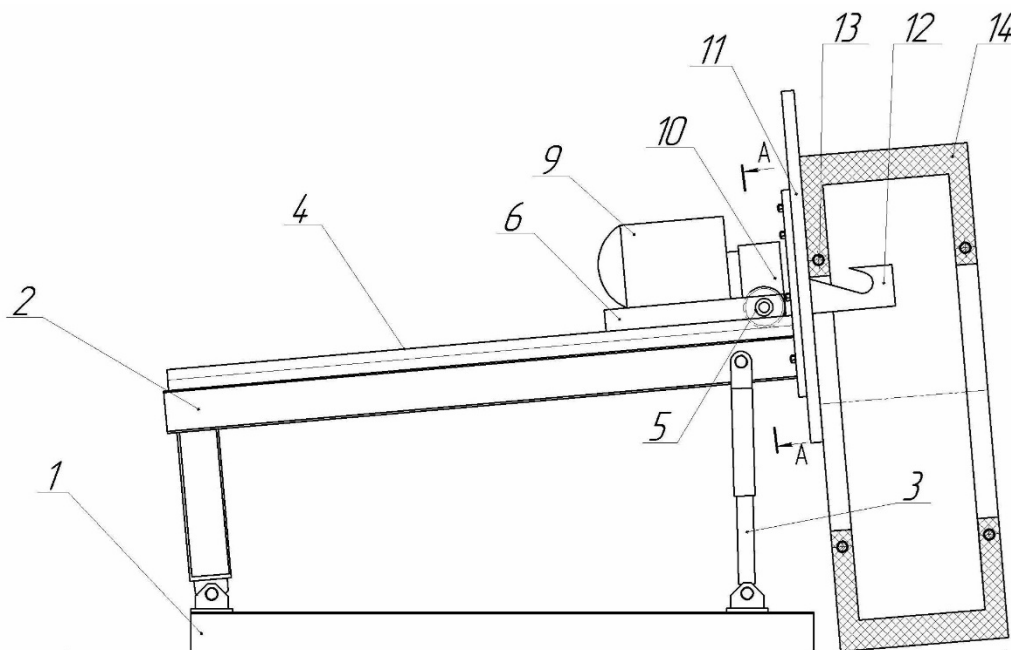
Общий вид установки для удаления троса из боковой части шины
